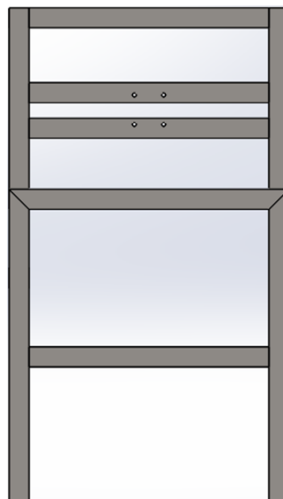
Diseño de los barrenos para la colocación de chumaceras en la estructura
